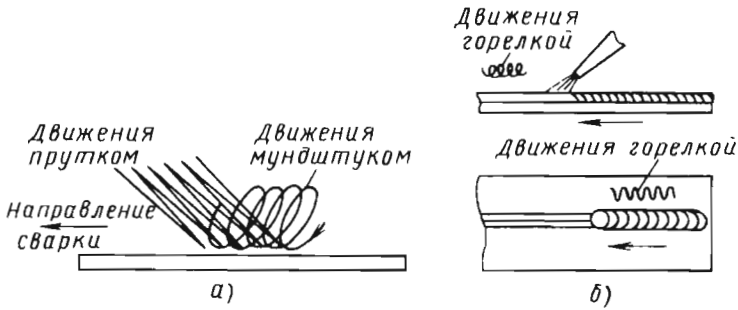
Сварка ванночками (а) и по отбортованным кромкам (б)
